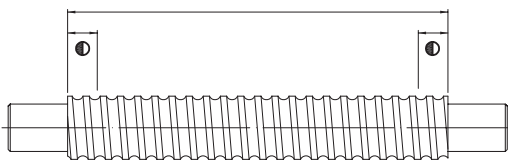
Bereich der Oberflächenhärtung einer Kugelgewindespindel
